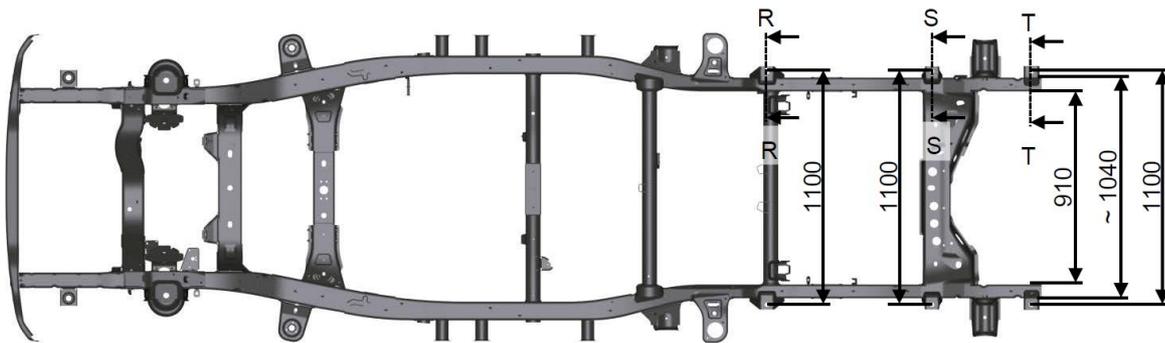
Vista de planta del bastidor Amarok DC
